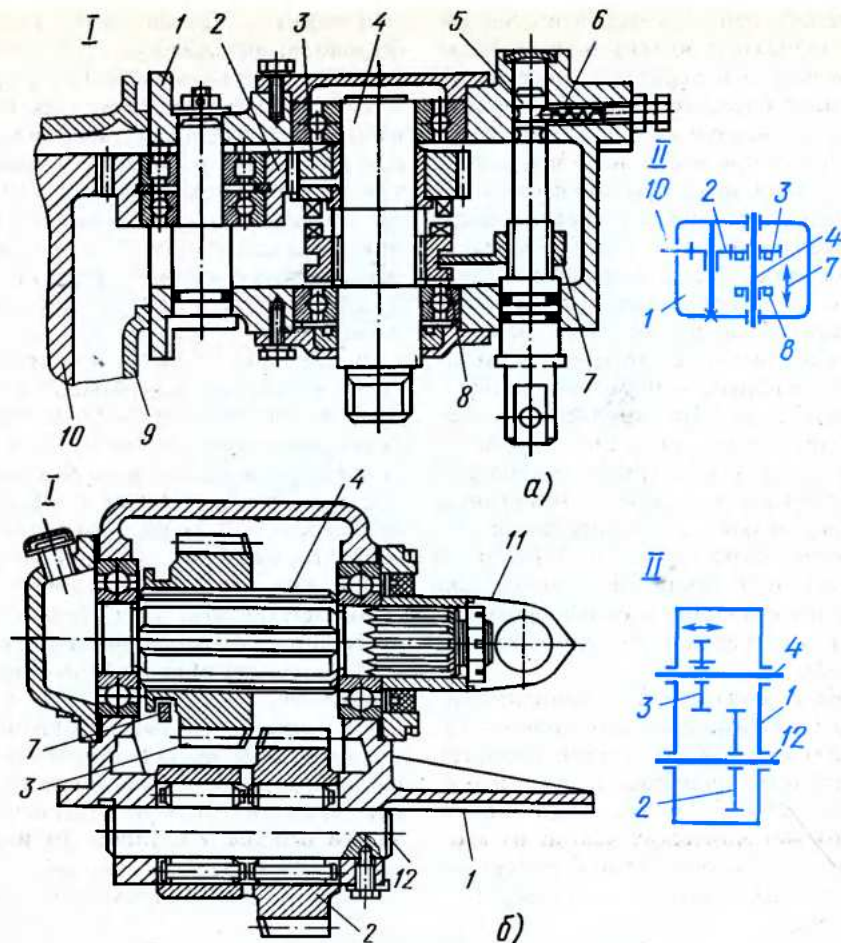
Коробки отбора мощности кранов КС-2561Д (а) и КС-4561А (б): I — общий вид, II — кинематическая схема; 1 — корпус, 2, 3 — шестерни, 4 — вал, 5 — валик, 6 — фиксатор, 7 — вилка, 8 — муфта, 9 — коробка передач автомобиля, 10 — шестерня, 11 — карданный вал, 12 — ось
